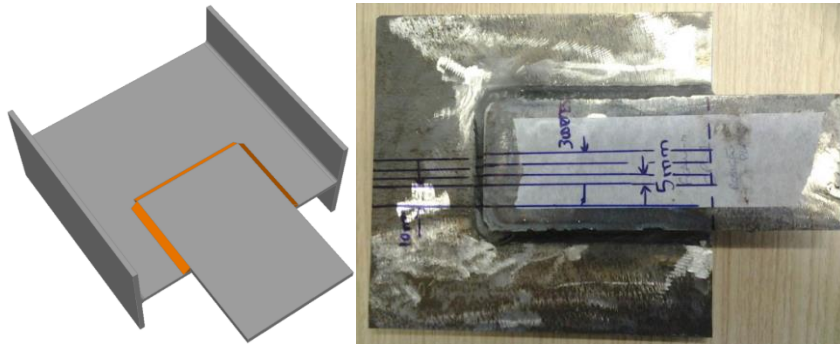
À esquerda: Croqui da junta analisada. À direita: Junta soldada pelo processo FCAW-s e marcada para o corte dos CPs para os ensaios.
